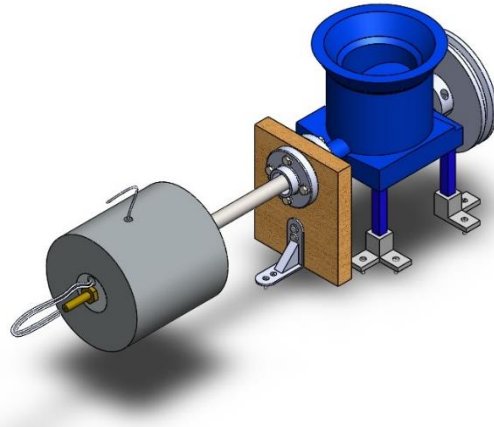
Montaje equipo de extrusión. Fuente: Propia.
